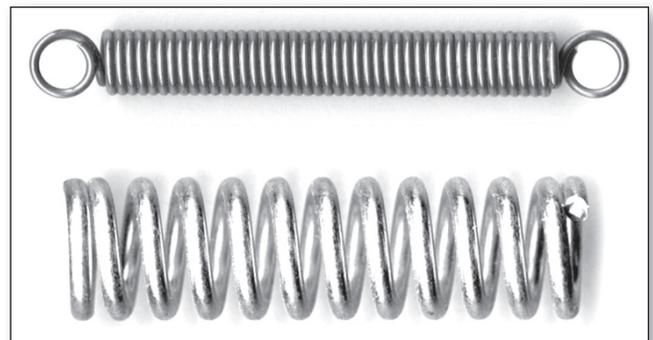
Zwei zylindrische Schraubenfedern: oben eine Zugfeder, unten eine Druckfeder
